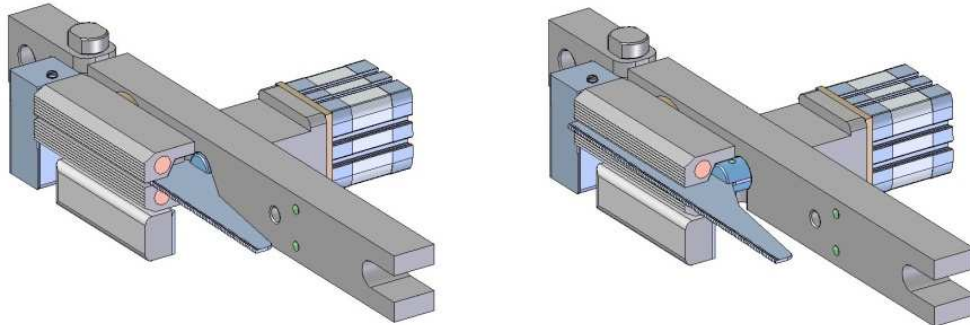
Detall de la soldadura horitzontal
